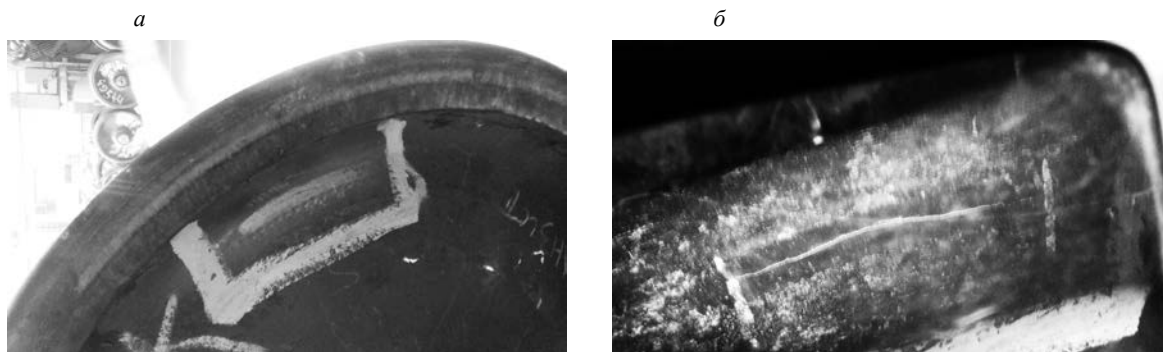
Трещина в диске вагонного колеса (а) и ее индикаторный след при магнитопорошковом контроле (б).
